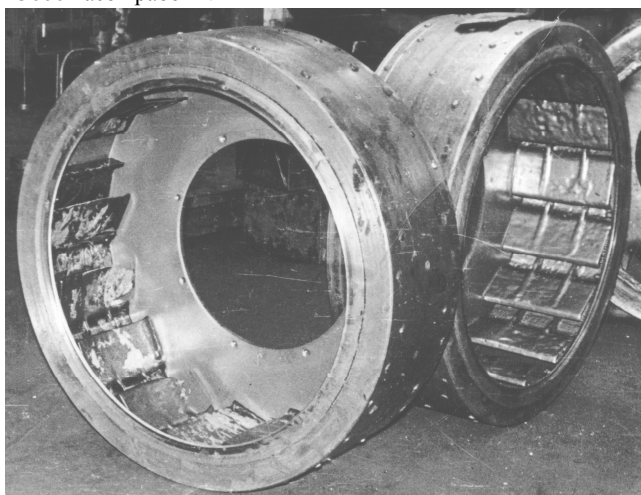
Элеваторы шарошлифовальных станков МШ-33: а - оборудованный ковшами из армированного древопласта; б - оборудованный ковшами из стального литья
